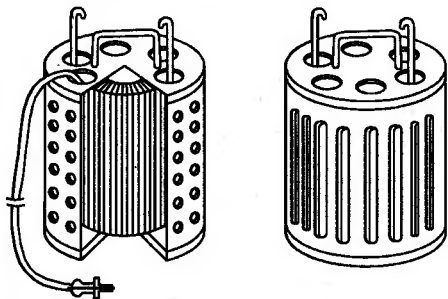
Варианты кожуха сварочного аппарата на основе «Латра»
